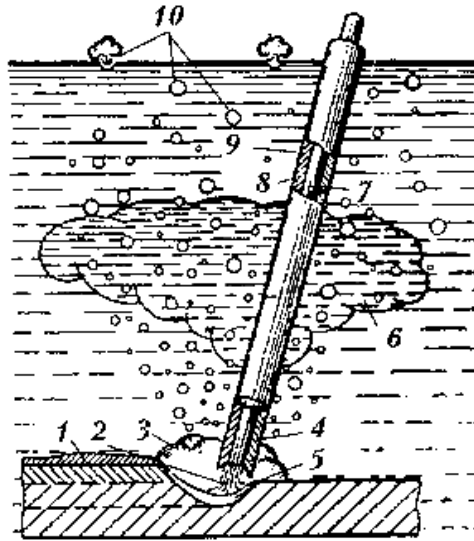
Схема мокрой сварки под водой: 1 – шлак; 2 – дуга; 3 – газовый пузырь; 4 – козырек электрода; 5 – сварочная ванна; 6 – облако мути; 7 – металлический стержень электрода; 9 – водонепроницаемый слой покрытия; 10 – пузырьки газа
